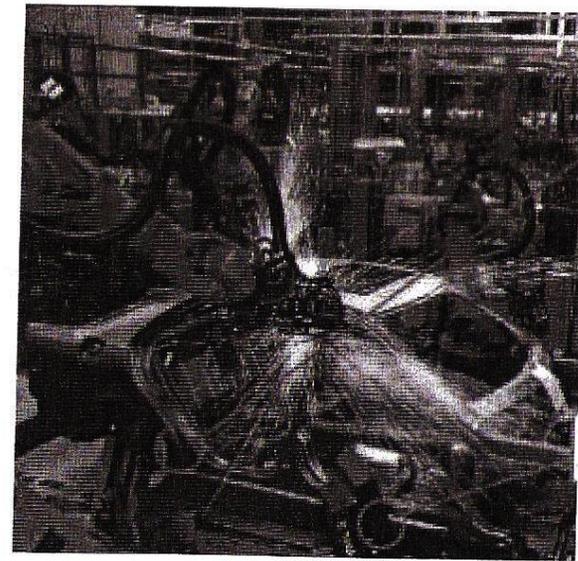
Proceso automático. Línea de soldadura robotizada.
